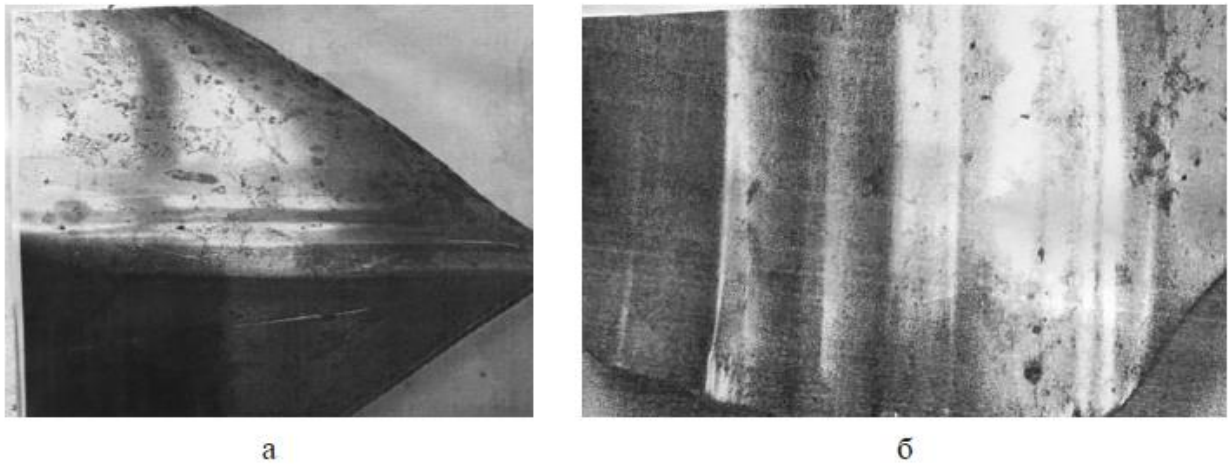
Характерне зношування носової частини зварних стрілочастих лап, виконаних зі сталі 50ХГА: а – у верхній частині в обробку кромки наплавлений сплав марки ПГ-С27; б – з двох сторін приварений зварювальним дротом Св08Г2С.
